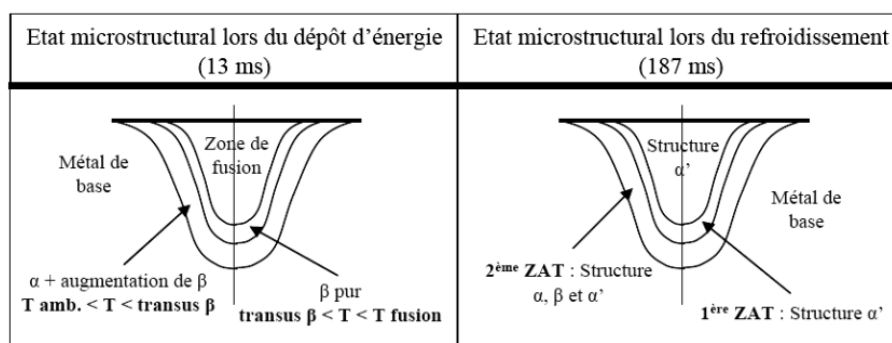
Analyse d'un cordon de soudure de TA6V pendant le soudage [23]
